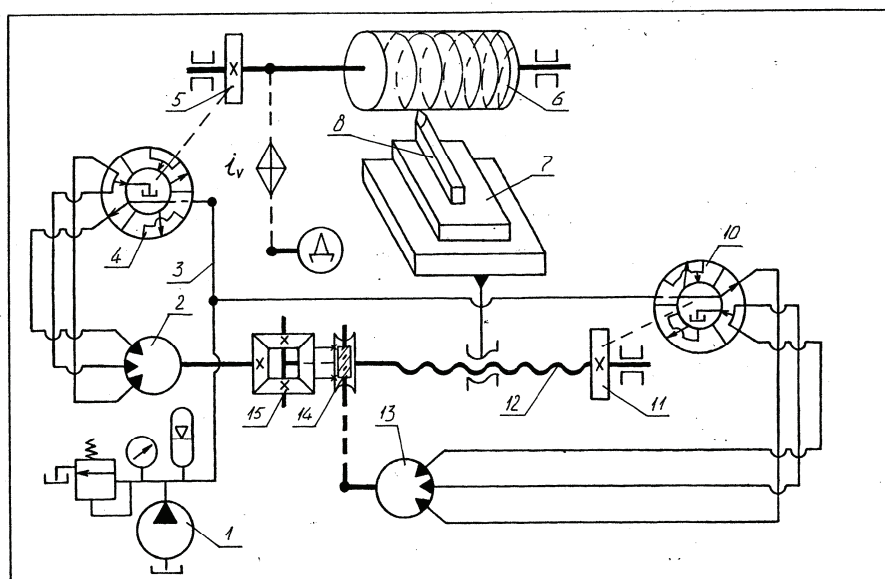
Резьбонарезной станок для нарезания цилиндрических винтовых поверхностей переменного шага
